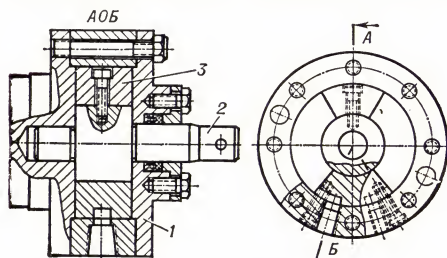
Моментный гидроцилиндр: 1 — корпус; 2 — вал; 3 — лопасть.
